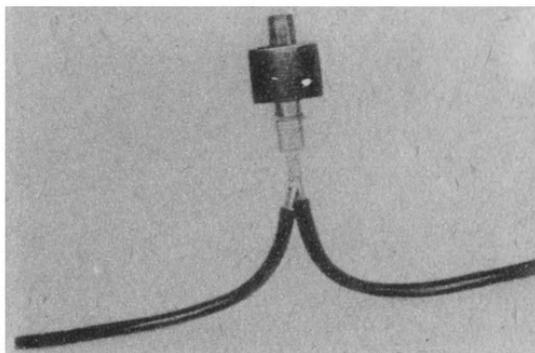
Подготовленные к сварке жилы кабеля с термитным патроном марки АС
